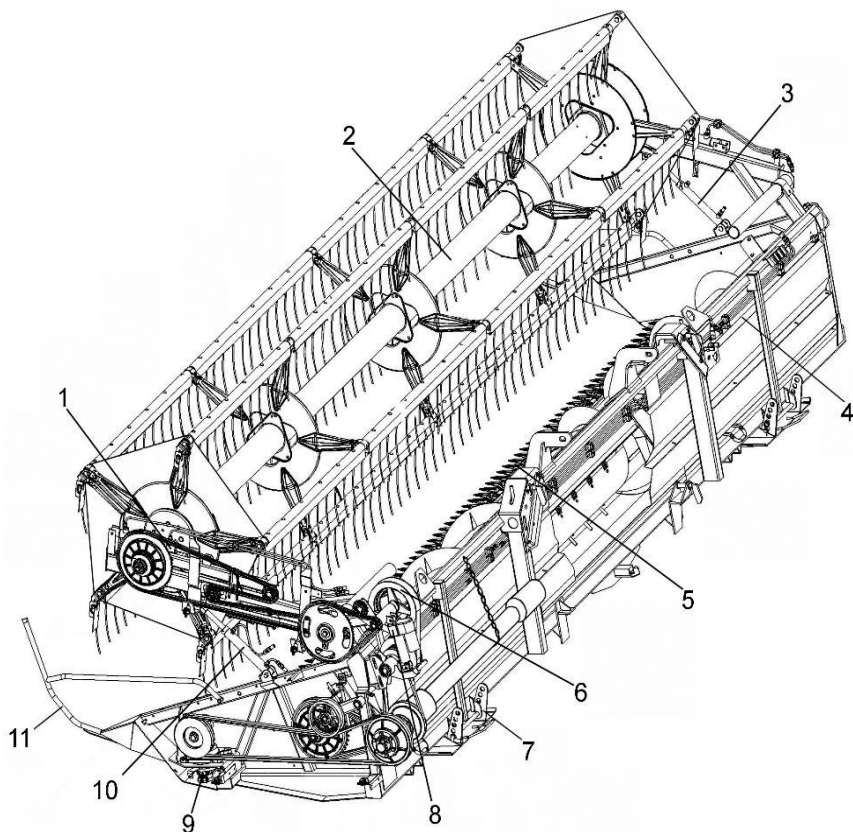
Жатка для зерновых культур: 1 – гидроцилиндр выноса мотовила; 2 – мотовило; 3, 10 – гидроцилиндры подъема мотовила; 4 – рама; 5 – режущий аппарат; 6 – вариатор; 7 – копирующий башмак; 8 – исполнительный электромеханизм; 9 – планетарный механизм привода режущего аппарата; 11 – делитель
